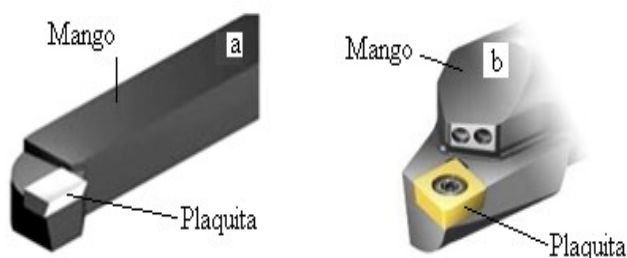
Portaherramientas con plaquita. (a) soldada, (b) intercambiable.
